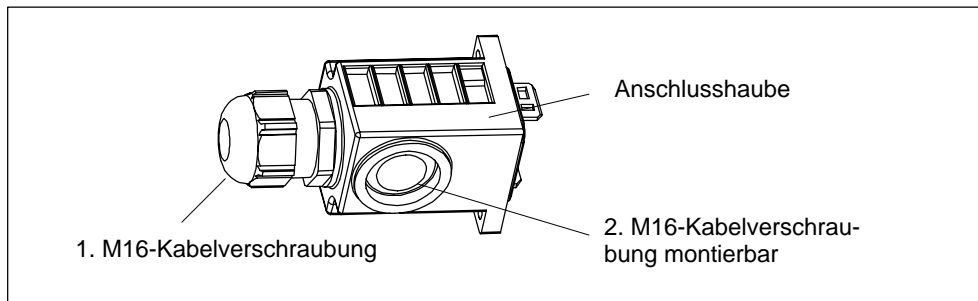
Anschlussstecker: Anschlusshaube mit einer M16-Kabelverschraubung
